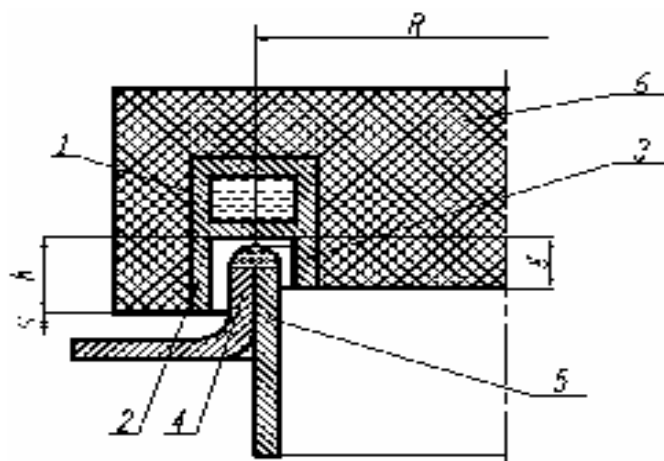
Поперечный разрез индуктора и свариваемого изделия
